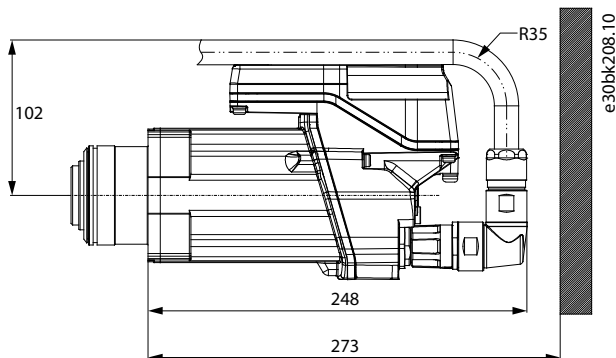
Mindestabstand für angewinkelten M23-Stecker
